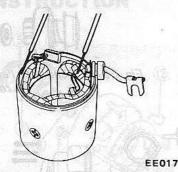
Contrôle de la masse du bobinage d'inducteur
